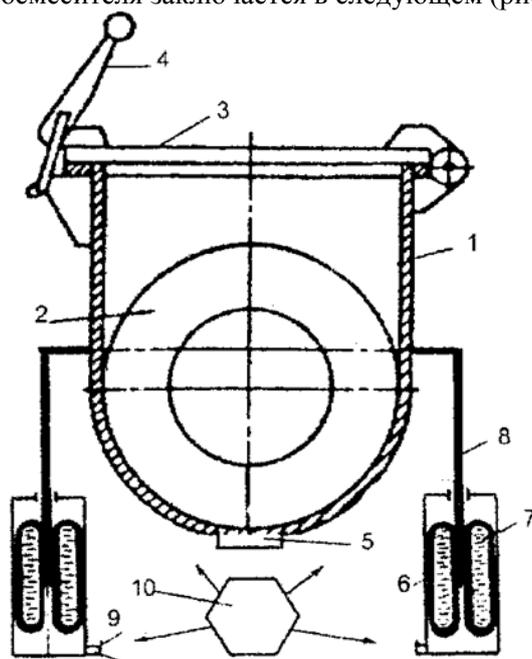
Вибросмеситель сыпучих компонентов: 1 - корпус; 2 - смешивательная емкость; 3 - загрузочная крышка; 4 - крепежная ручка; 5 - разгрузочный патрубок; 6 - вибровозбудитель цилиндрической формы; 7 - эластичный тороид; 8 - шток; 9 - шланги; 10 - блок управления
